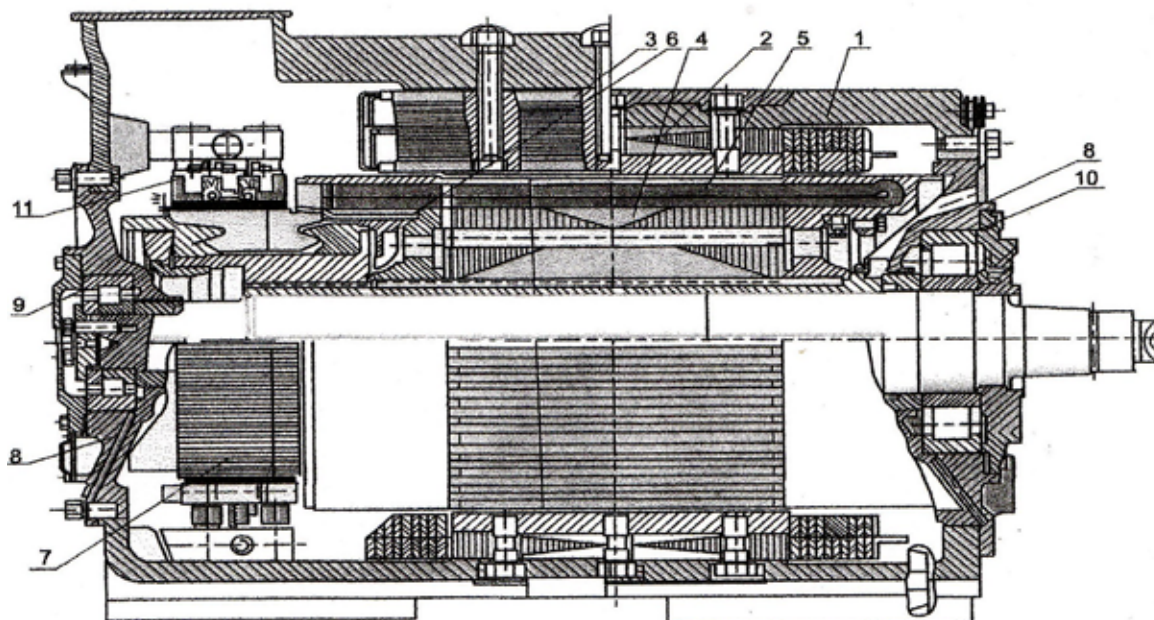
Двигатель постоянного тока тяговый универсальный ЭДУ-133
